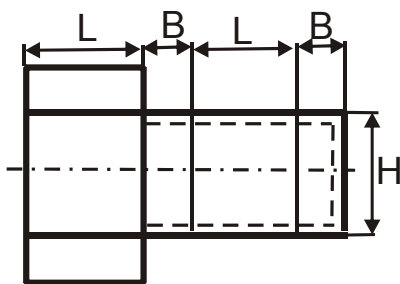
Розгортка листового матеріалу для виготовлення бака
